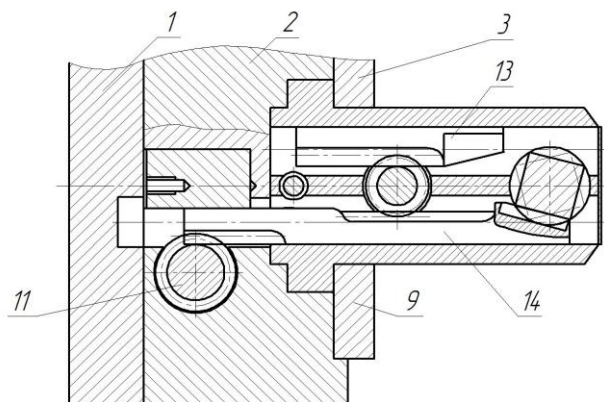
Конструкция поворотного патрона с клиновым устройством зажима
